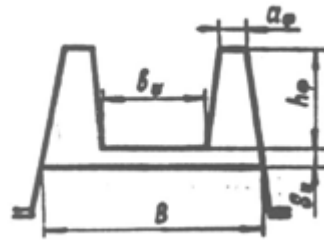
Профиль швеллерного типа с закрытыми фланцами
